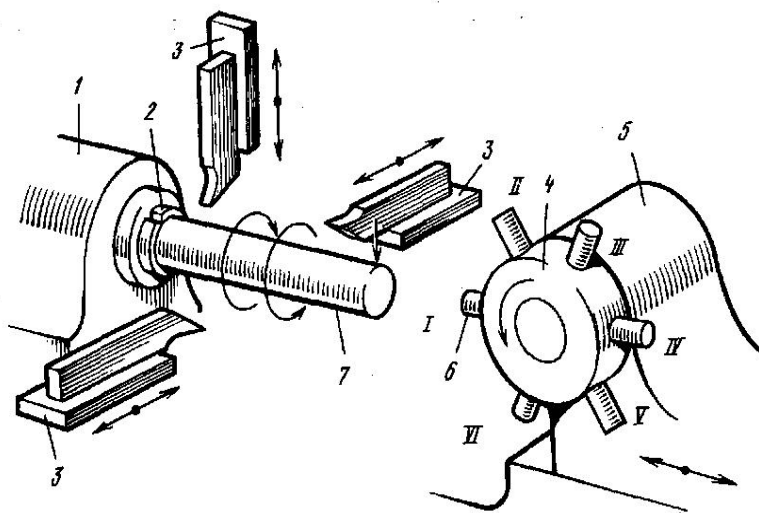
Схема роботи токарно-револьверного автомата
